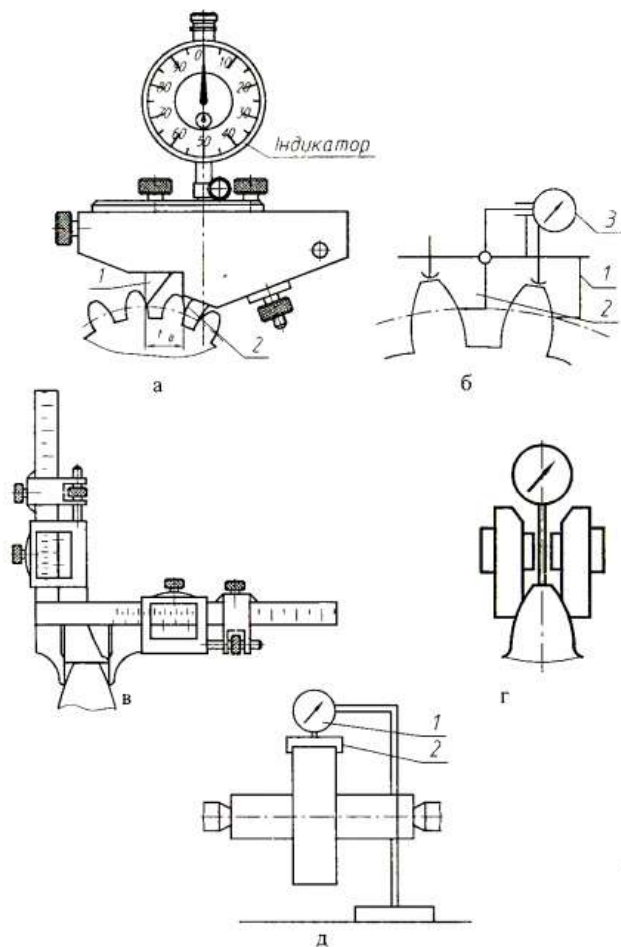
Контроль зубчастих коліс: а, б – контроль кроку зубів; в – контроль товщини зуба по початковій лінії за допомогою штангензубоміра; г – контроль товщини зуба по початковій лінії за допомогою індикаторного пристрою; д – контроль радіального биття зубчастого вінця
